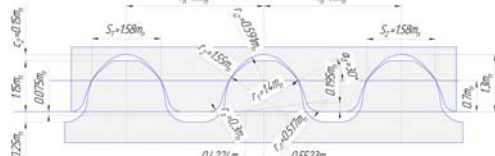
Исходные формообразующие контура для зубчатого колеса и шестерни зубчатой передачи с профилем Новикова
